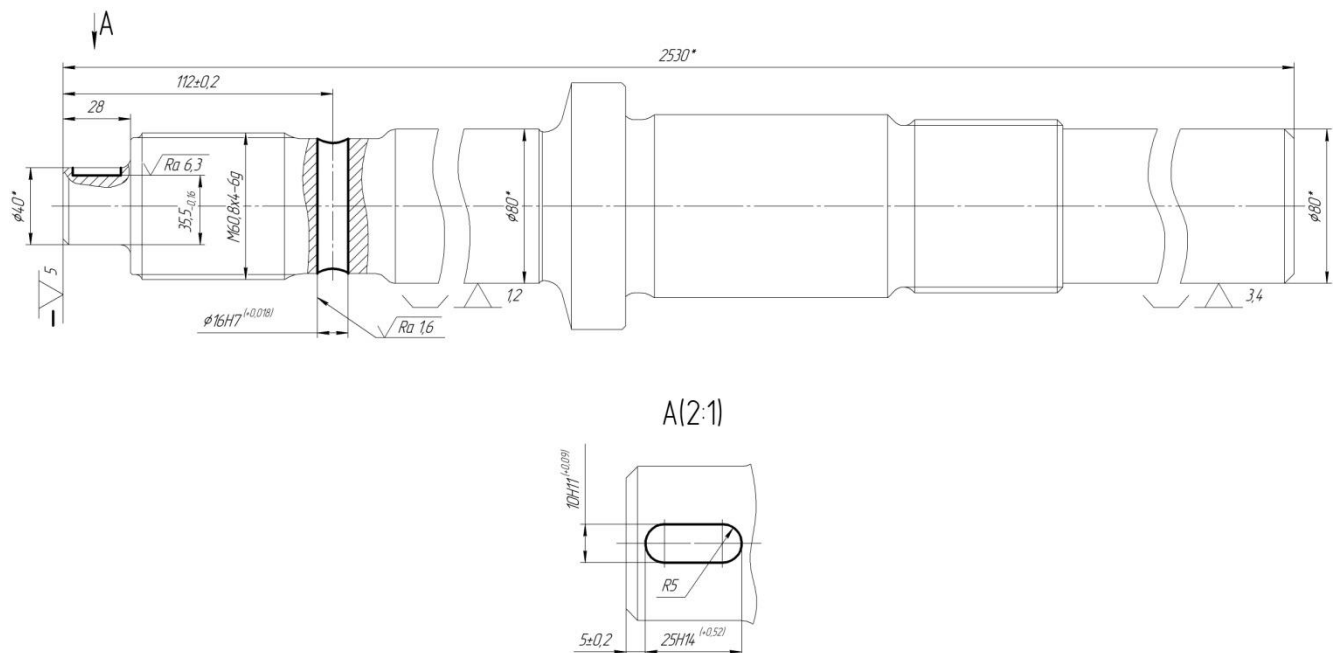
Схема базування заготовки на комплексній з ЧПК операції (перший варіант)
